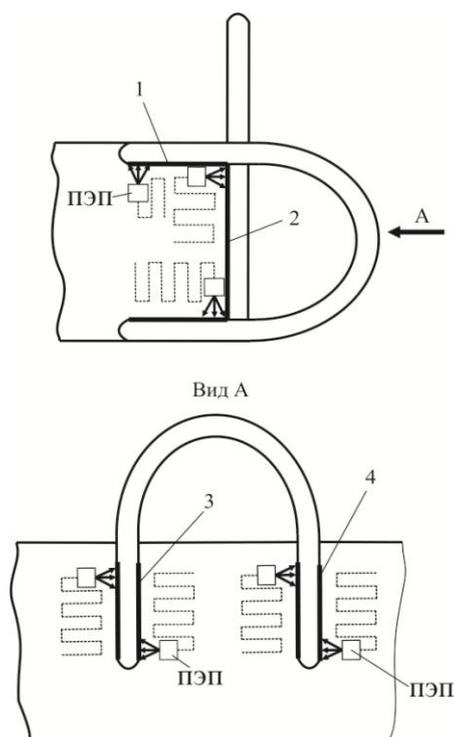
Схема УЗК сварных швов мест приварки проушин к раме стрелочного перевода
